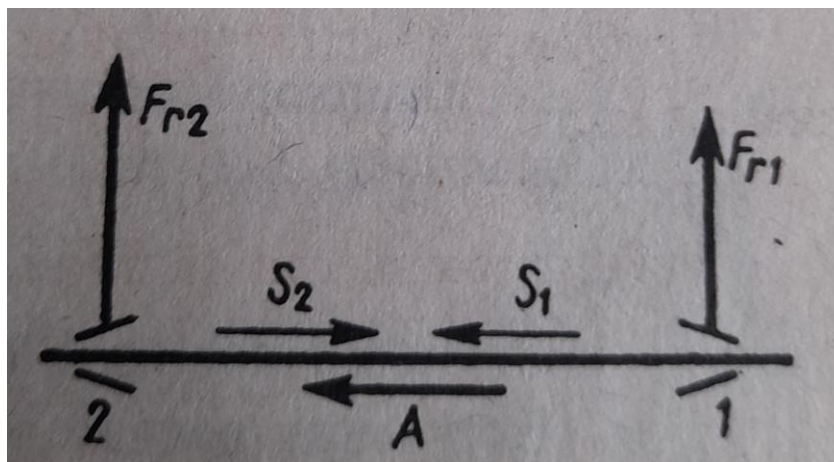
Схема расстановки осевых сил для радиально-упорных подшипниковых опор
